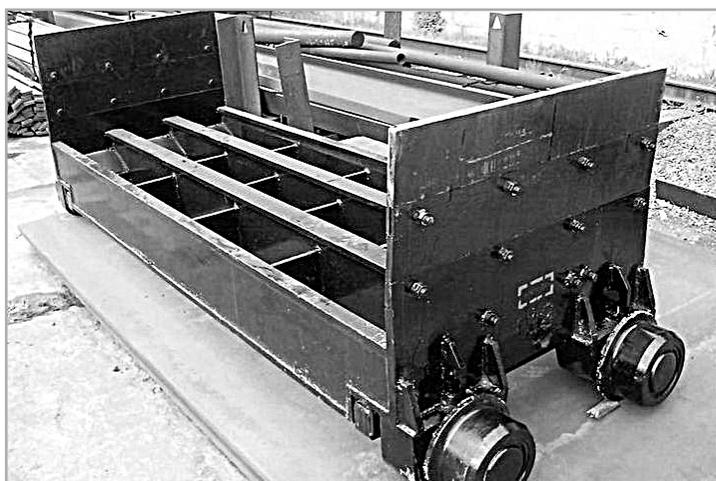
Общий вид прокатно-сварной спекательной тележки
